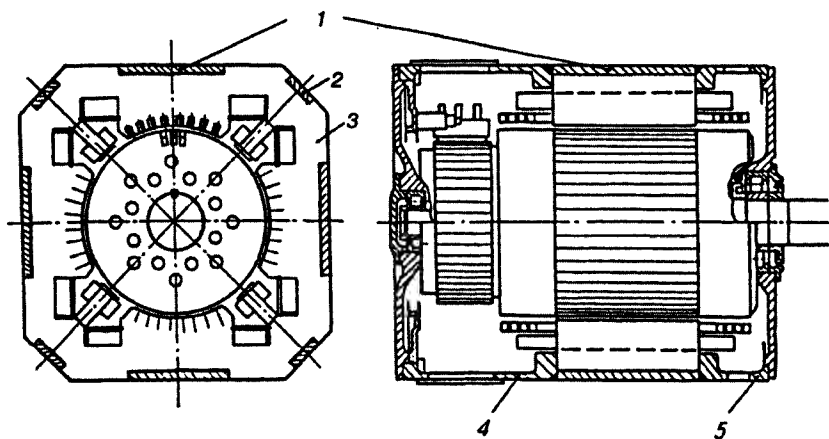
Бескорпусная конструкция коллекторного ТЭД
